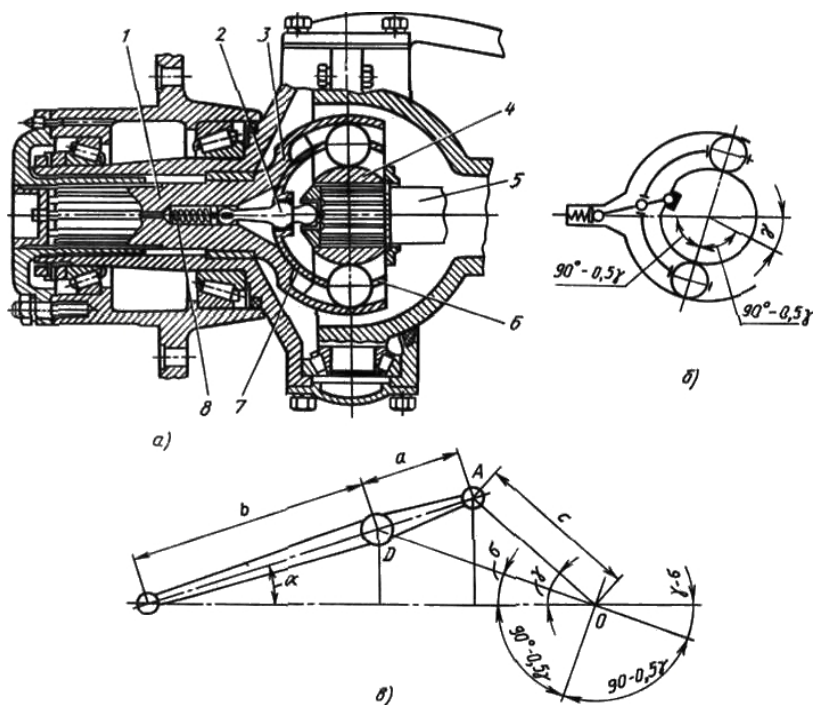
Карданный шарнир типа «Рцепп»: а — конструкция; б — схема; в — схема рычажка; 1, 5 — валы; 2 — делительный рычажок; 3 — сферическая чашка; 4 — сферический кулак; 6 — сепаратор; 7 — направляющая чашка; 8 — пружина
